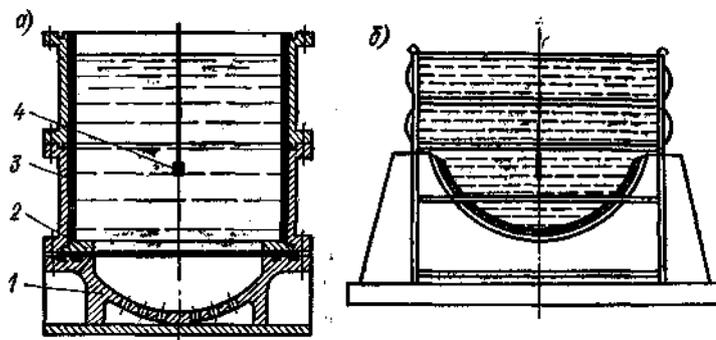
Съемные установки для штамповки взрывом небольших деталей
